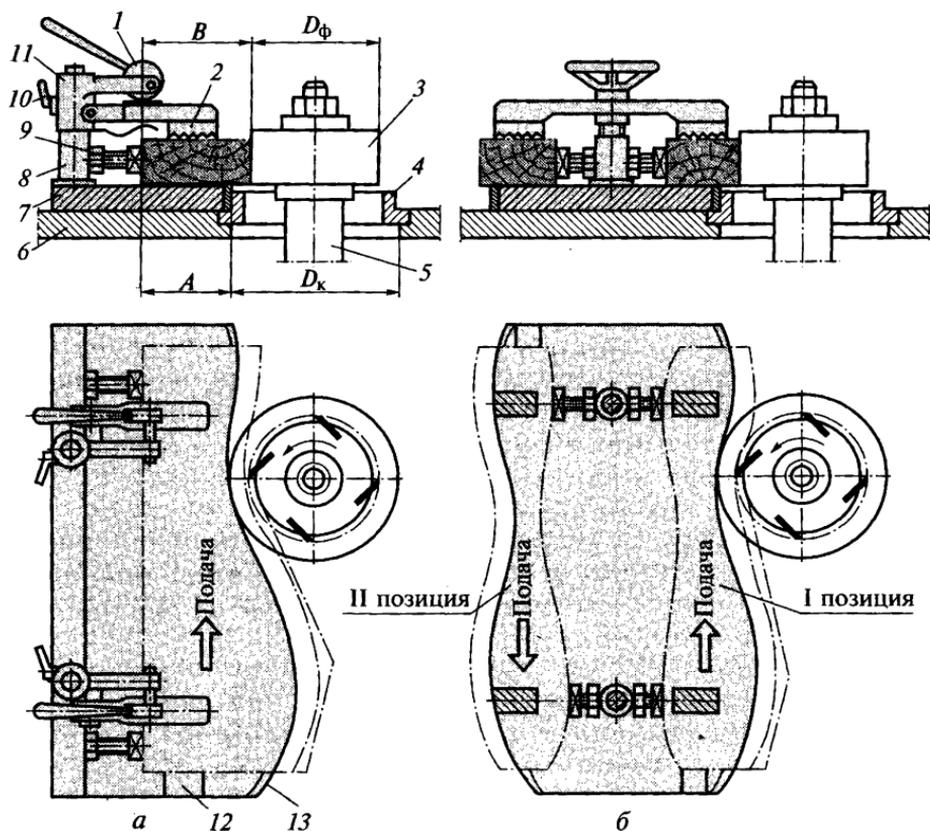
Схема криволинейной обработки на фрезерном станке с помощью шаблона:
